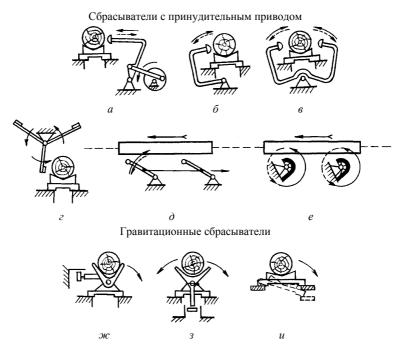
Схема сбрасывателей бревен с продольных конвейеров: a — рычажный с поступательно-возвратным движением; δ , ϵ — с поворотно-возвратным движением; ϵ — шаговый с вращательным движением в вертикальной плоскости; ϵ — с поворотно-возвратным движением в горизонтальной плоскости; ϵ — кулачковый с вращательным движением в горизонтальной плоскости; ϵ — с одно- и двухсторонним опрокидыванием опоры; ϵ — с наклонам грузонесущей поперечины
